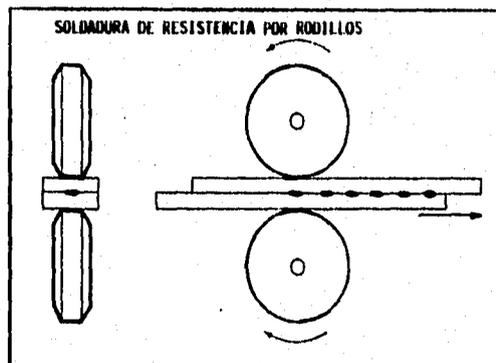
ESQUEMA DE SOLDADURA DE RESISTENCIA POR RULETAS.
